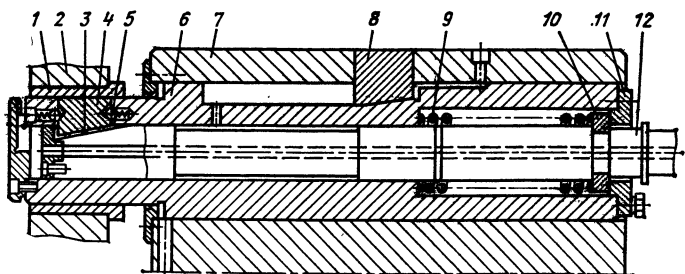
Цилиндрический фиксатор с выборкой зазоров
